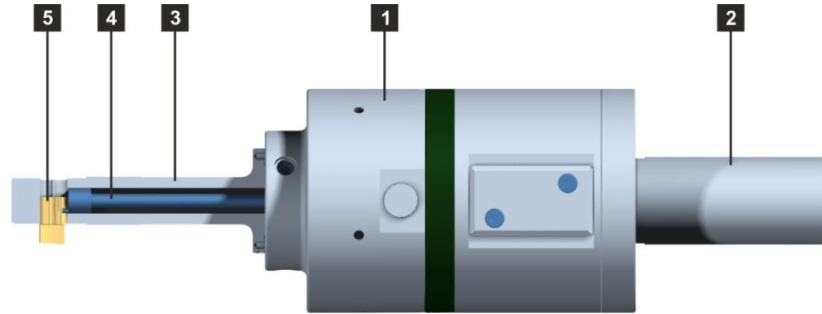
Приклад обробки поверхні, яка знаходиться з протилежного боку від шпинделя верстата
